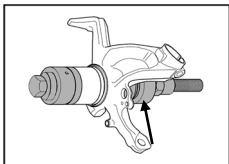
KL-0040-2500 - Hydraulik-Zylinder
